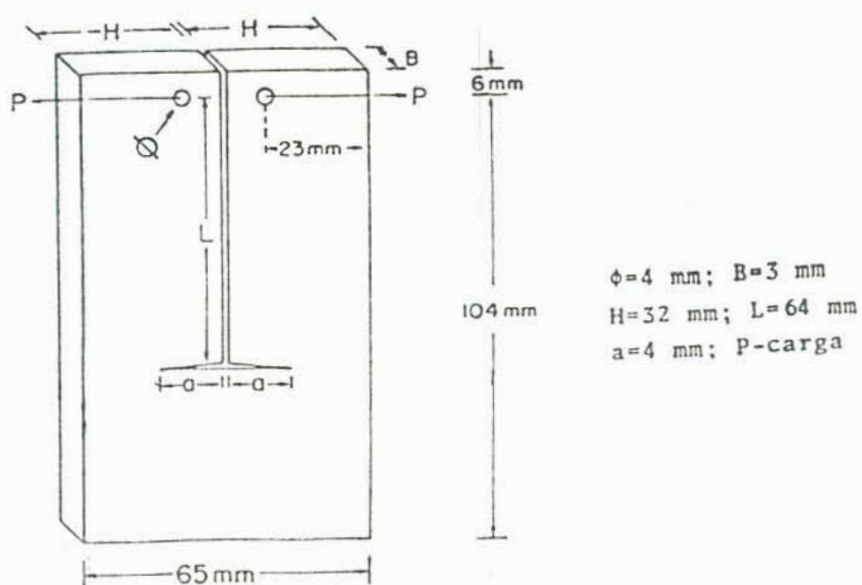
Dimensões e geometria do c.p. TN-DCB ^{65, 68, 70}
